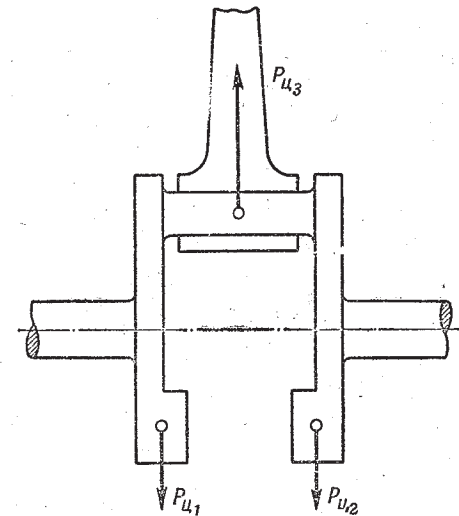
Силы инерции в кривошипном механизме одноцилиндрового двигателя
